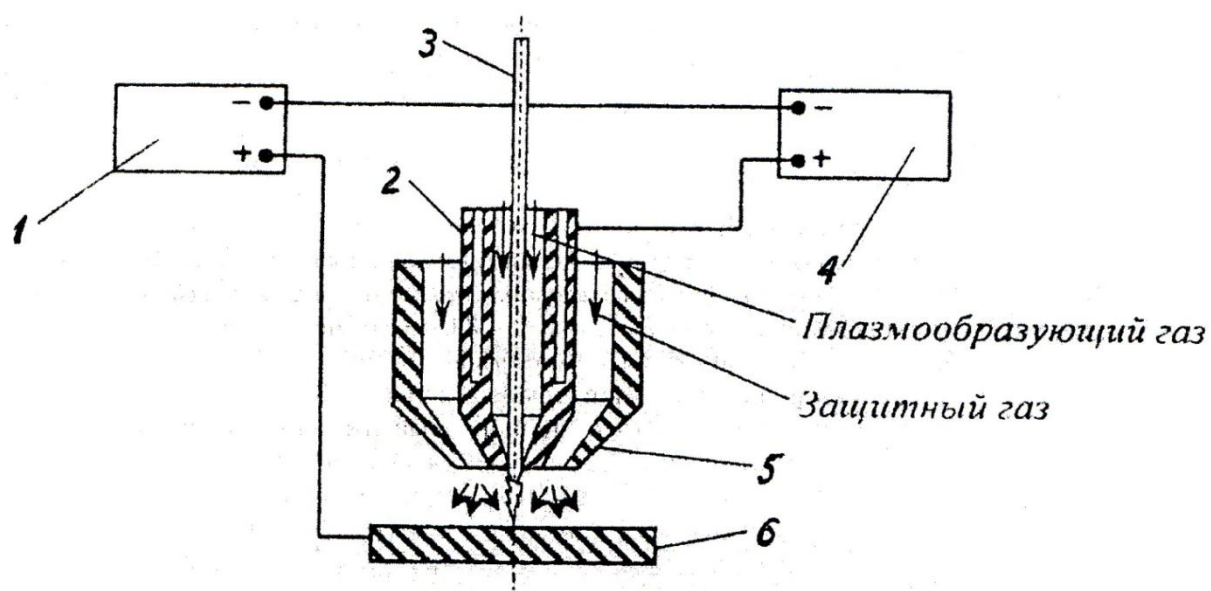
Схема процесса микроплазменной сварки металлов:
